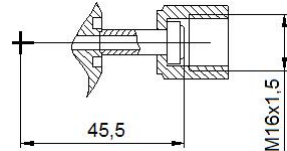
Штуцер (выходной) для торцевого уплотнения Ni шайбой с гайкой с метрической резьбой M16x1,5
